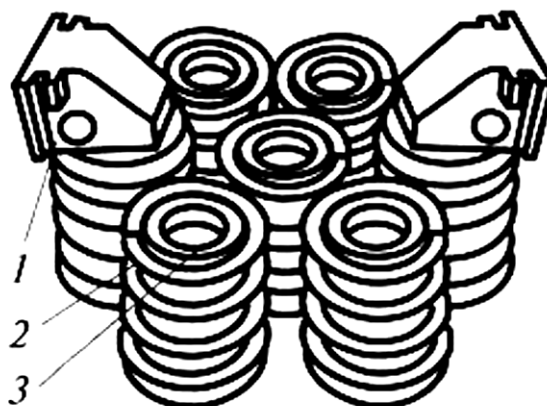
Общий вид рессорного комплекта тележки 18-100: 1 — фрикционный клин, 2 — наружная пружина, 3 — внутренняя пружина
